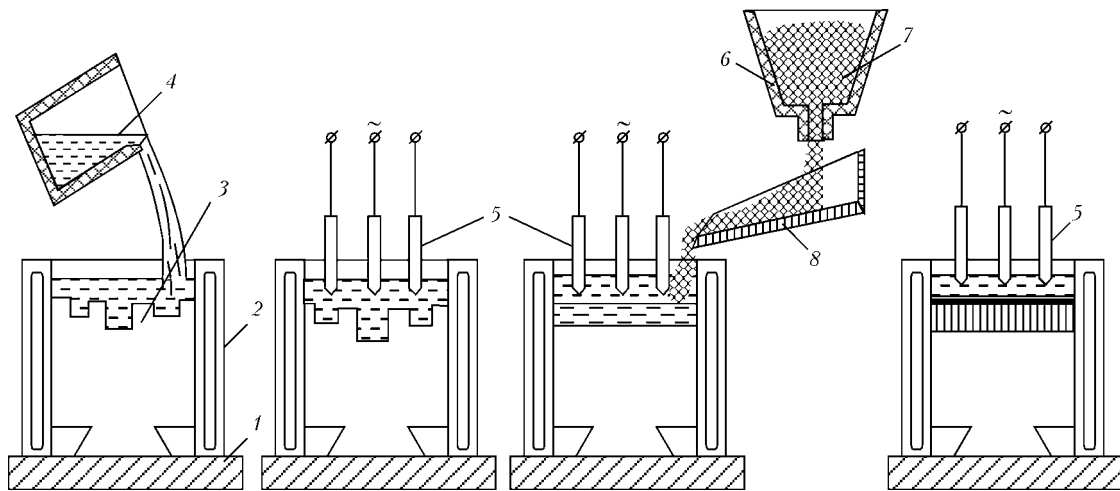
ЭШН штампов с использованием стружки инструментальной стали: 1 — поддон; 2 — неподвижный кристаллизатор; 3 — изношенный штамп; 4 — ковш с жидким шлаком; 5 — неплавящиеся электроды; 6 — дозатор; 7 — стружка; 8 — желоб
